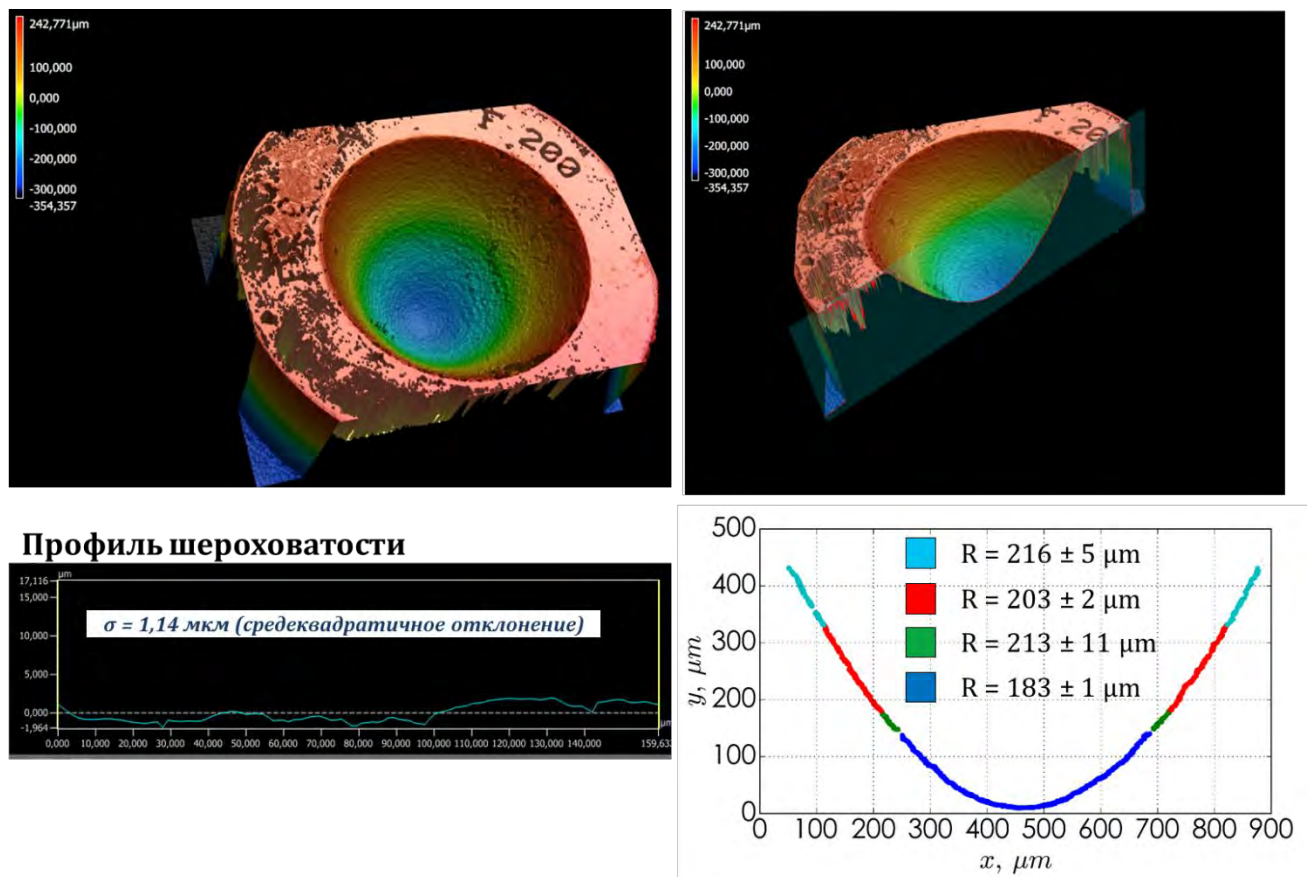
3D Сканирующий лазерный конфокальный микроскоп позволяет восстановить трехмерную модель двумерной полу-линзы, исследовать профиль поверхности и оценить шероховатости.
